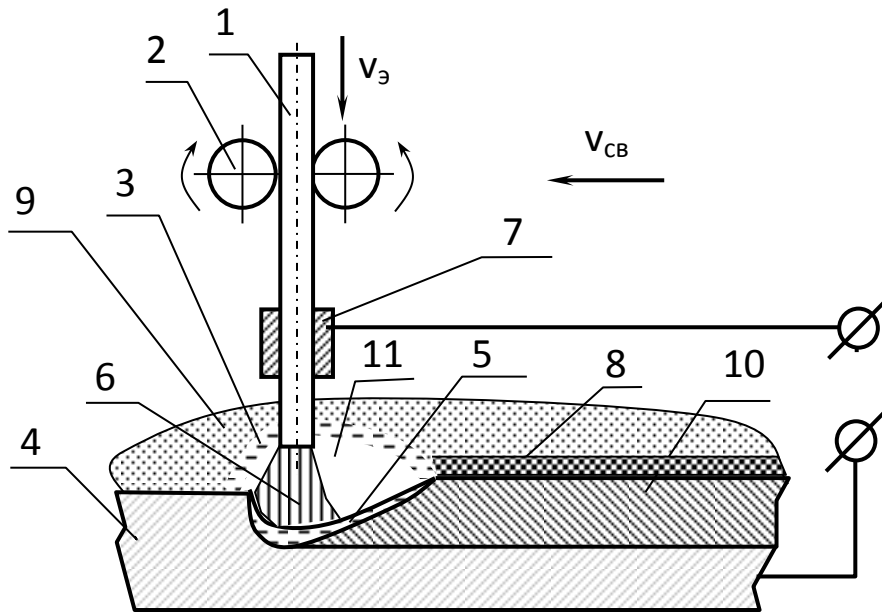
Схема дуговой сварки под флюсом
